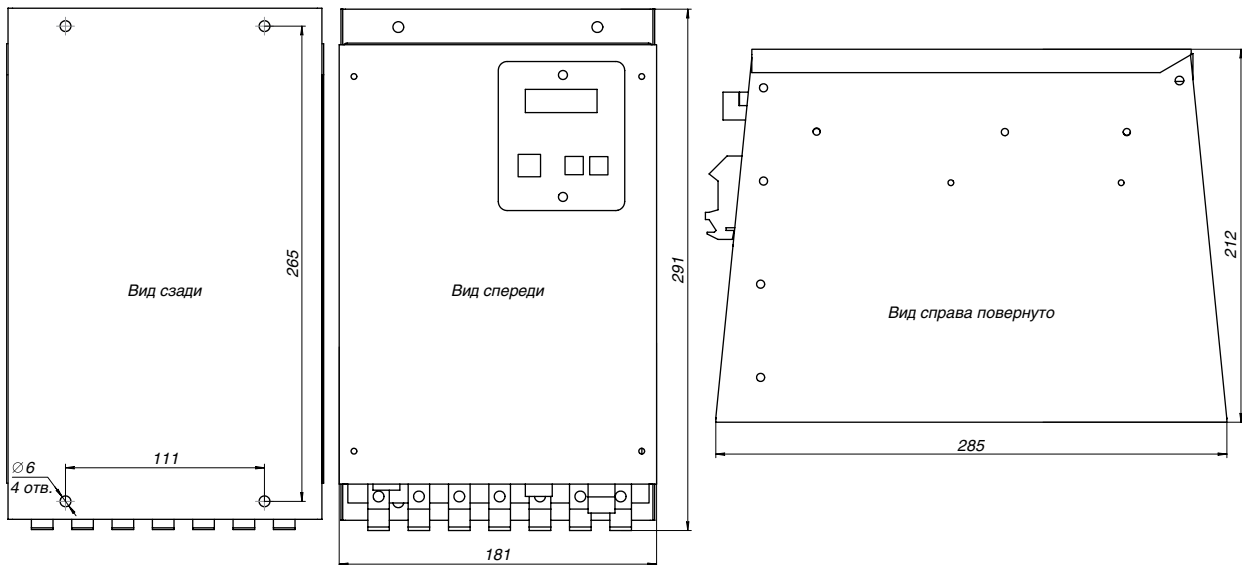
Общий вид, габаритные размеры (мм) регулятора первого типоразмера
